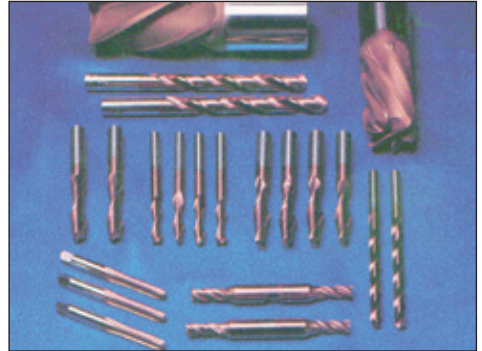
Mit Titan-Aluminium-Nitrid beschichtete Werkzeuge (Hilti AG)
